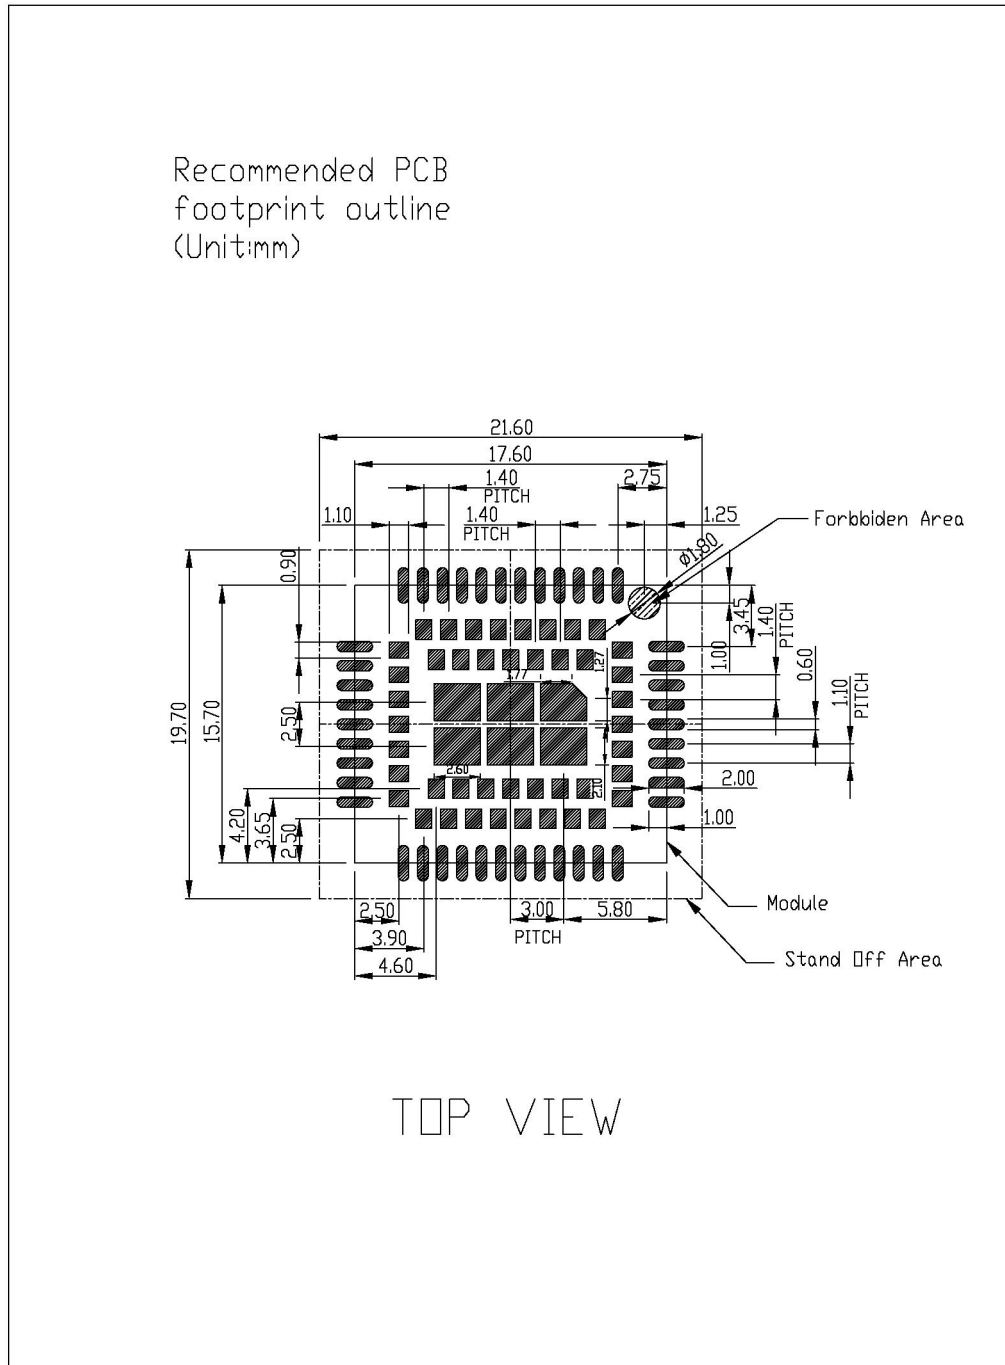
推荐 PCB 封装尺寸 (单位: 毫米)
